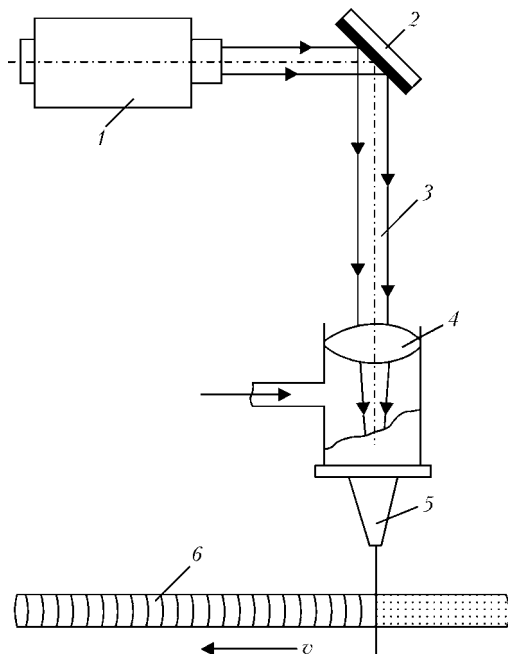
Схема системы СО₂-лазера для обработки металлов: 1 — источник лазера; 2 — зеркало; 3 — луч лазера; 4 — линза; 5 — сопло; 6 — деталь
